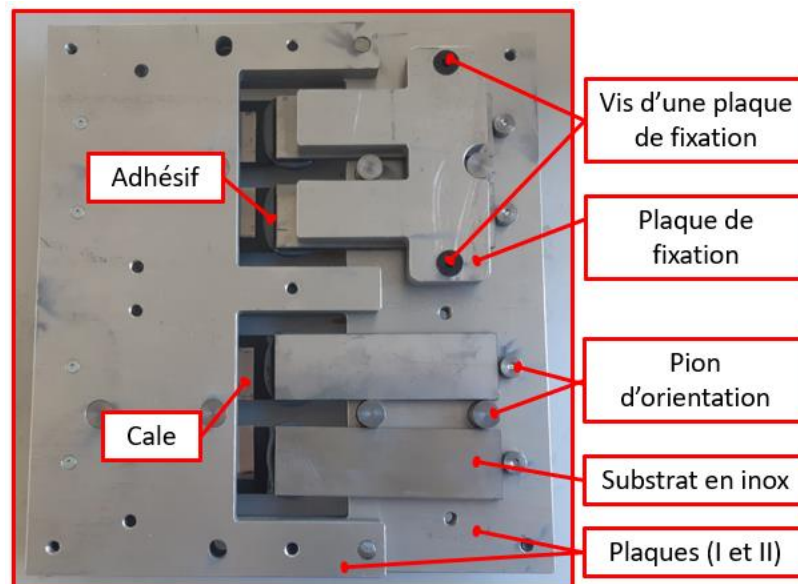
Dispositif de collage pour l'assemblage des éprouvettes joints à simple recouvrement
